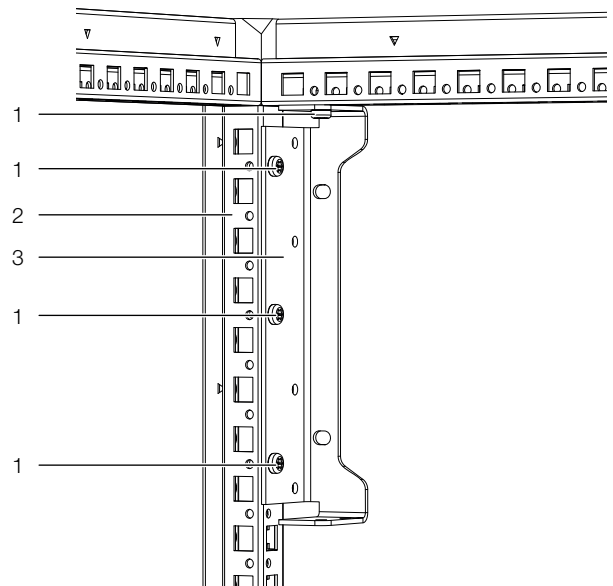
Befestigung des oberen Abfangwinkels am Schrank
